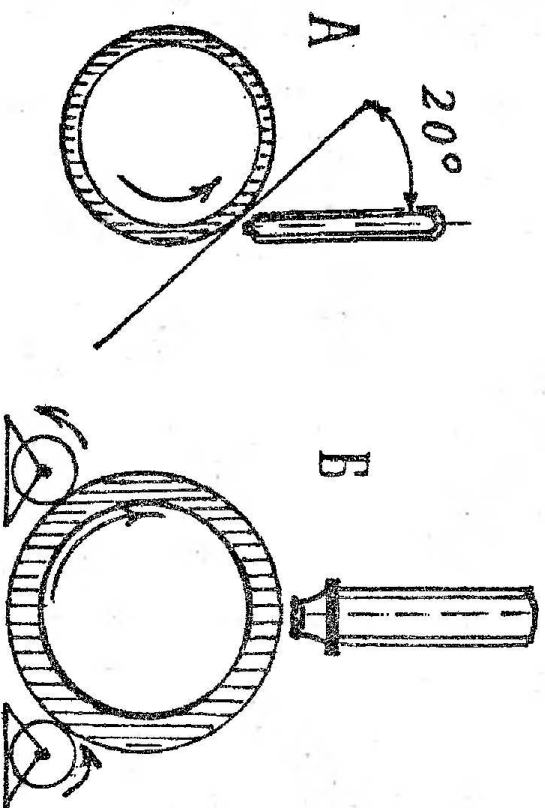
Резка труб. А — скоростная резка; Б — резка на роликовом стенде
